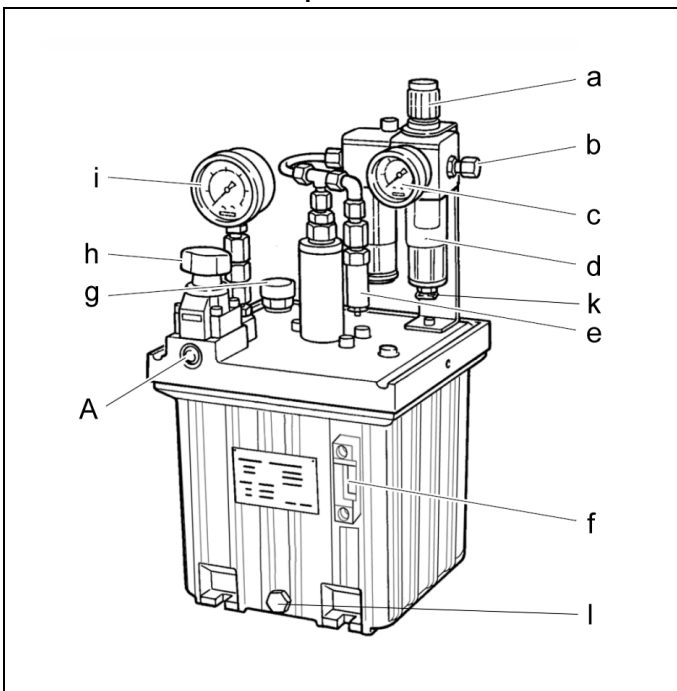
Prinzipabbildung, Komponenten je nach Bauart
